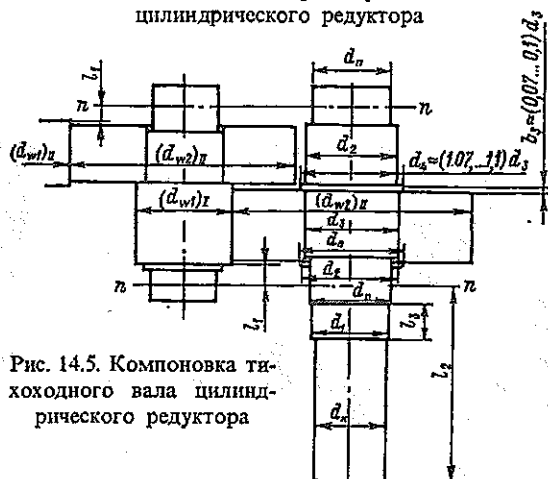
Компоновка тихоходного вала цилиндрического редуктора
